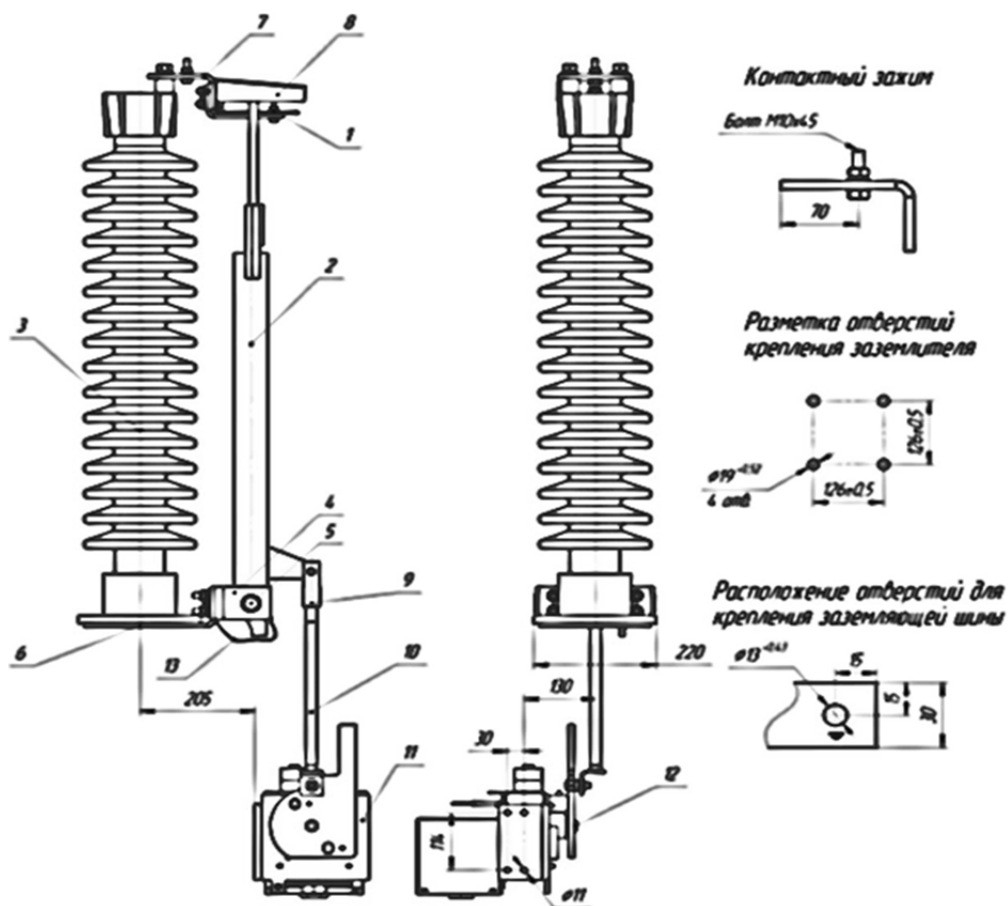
Общий вид заземлителя ЗОН и привода
